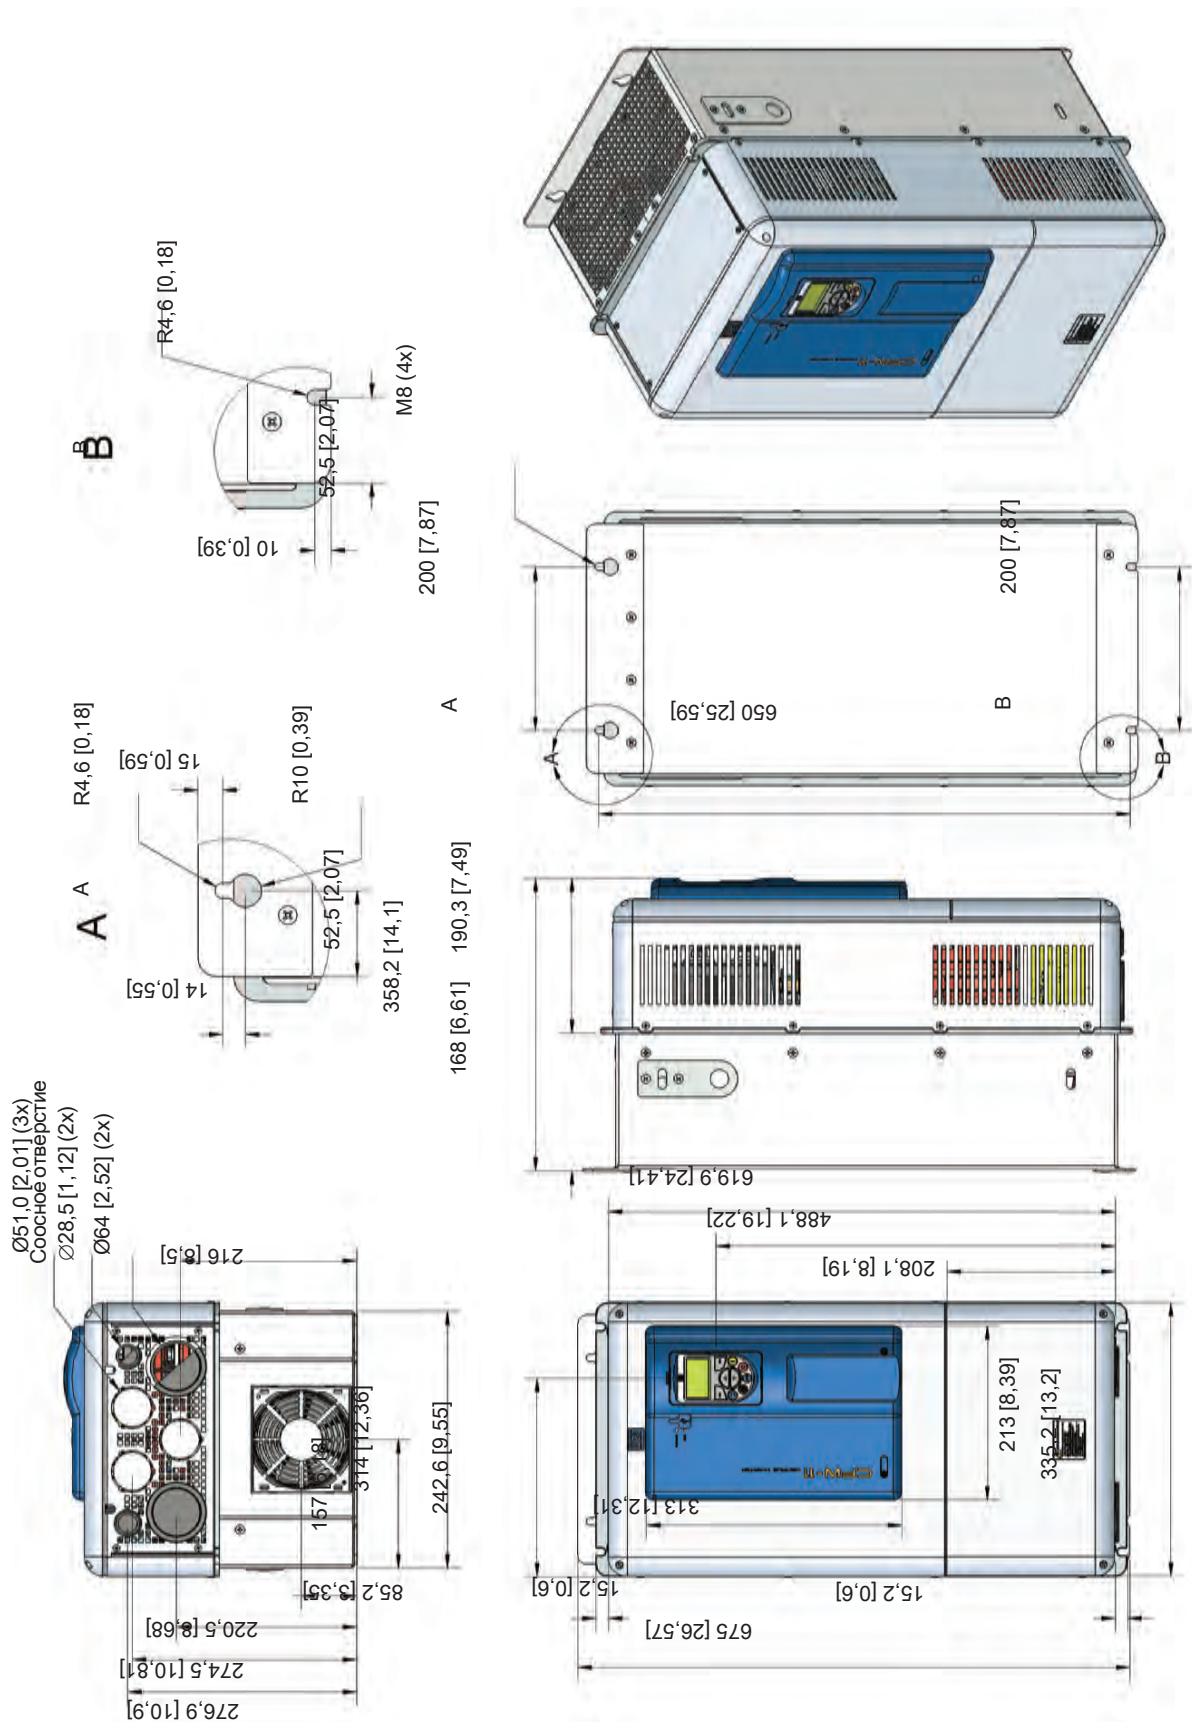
Габаритные размеры преобразователя, размер корпуса E, мм [дюйм.]
